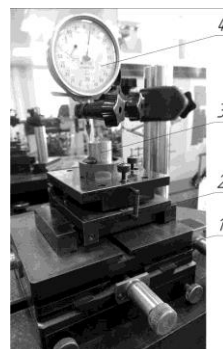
Приспособление для измерения размеров наплывов металла на торцах образцов:
